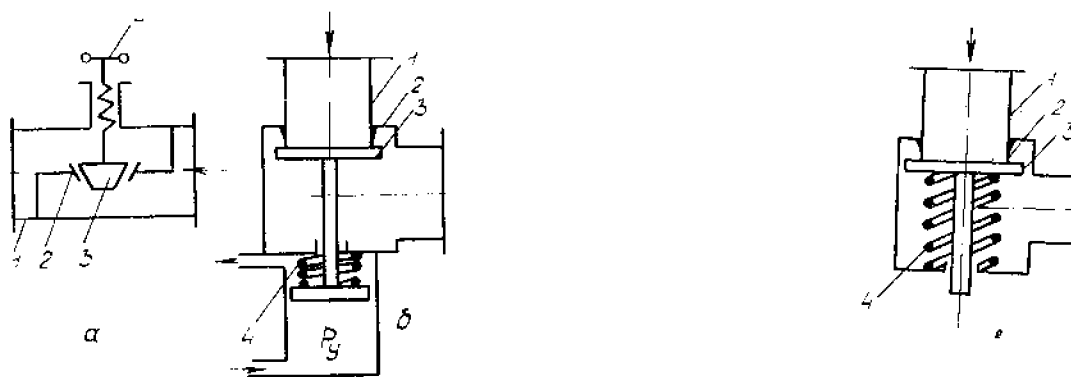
Виды клапанных устройств: а- с ручным; б- с дистанционным управлением; в – автоматическое; 1 – корпус; 2- седло; 3- запорный орган; 4 — привод
